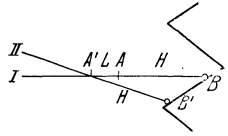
Messung des Flankenwinkels großer Gewinde.
